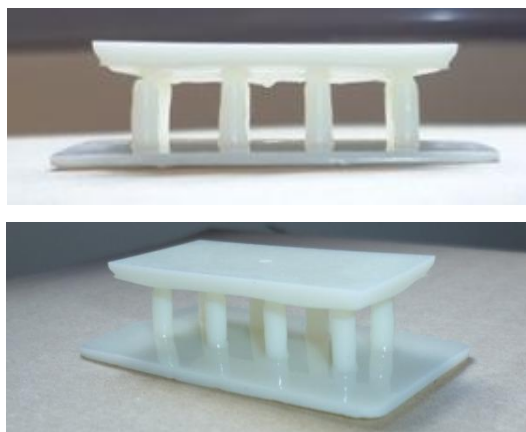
Pieza probeta 4. Arriba, vista frontal. Abajo, vista isométrica.
